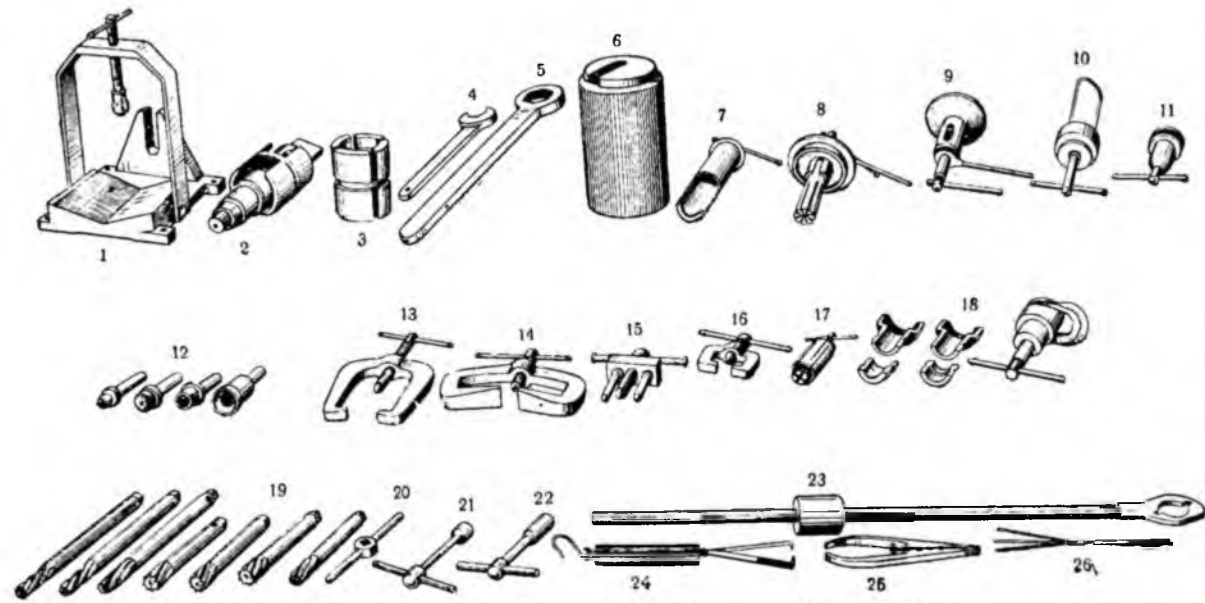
Комплект приспособлений марки РМ-1 ВИМЭ.
